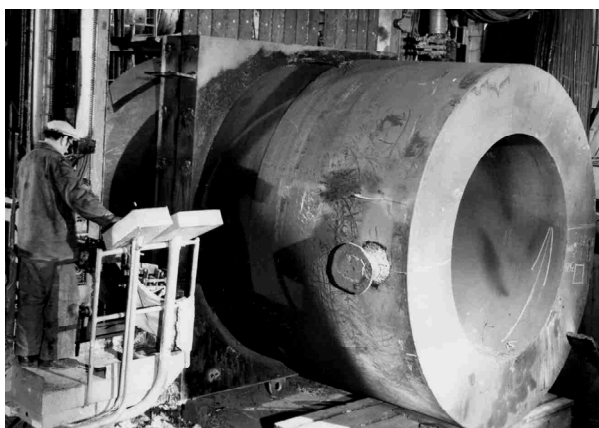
Электрошлаковая сварка цилиндра с применением выравнивающего квадрата (70-е годы 20 в.)
